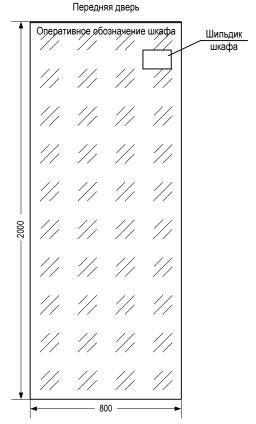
Общий вид обзорной двери типового шкафа
